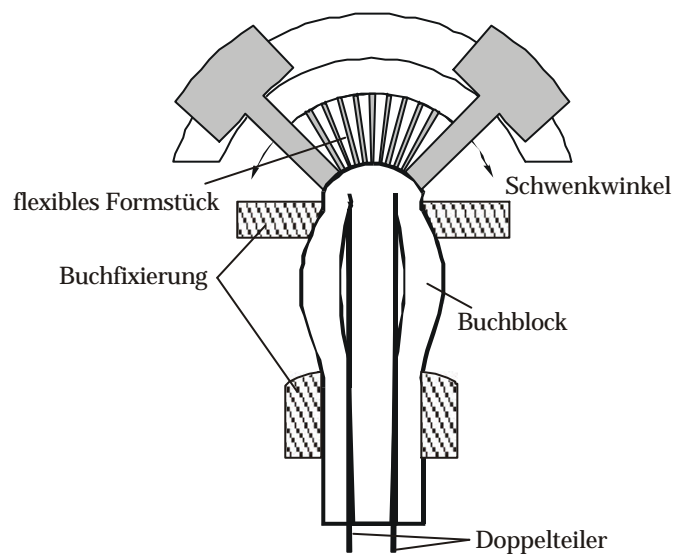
Rundepinzip mittels schwenkbarem Formelement
